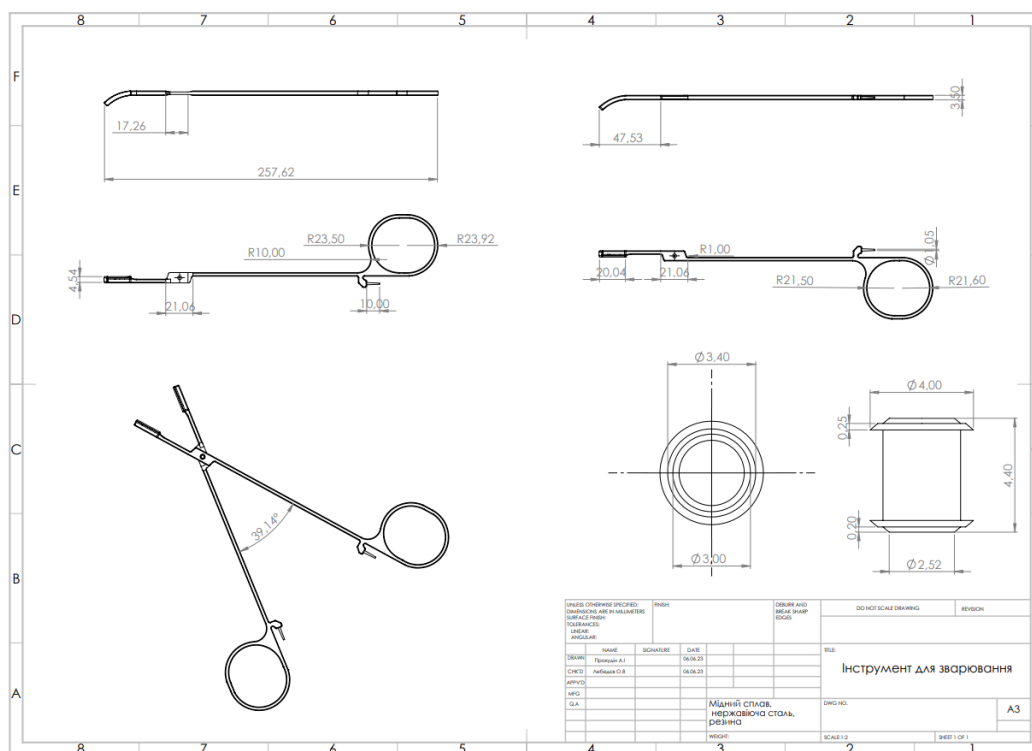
Кресленик інструменту створений в середовищі Solidworks
